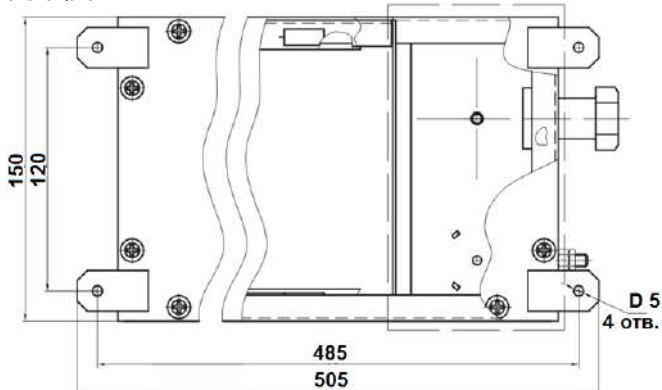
Габаритные и посадочные оповещателя «Плазма»П220
